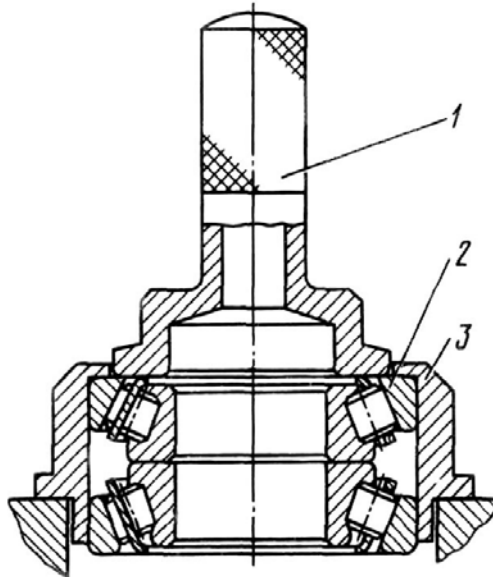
Выпрессовка роликовых подшипников из гнезда:
